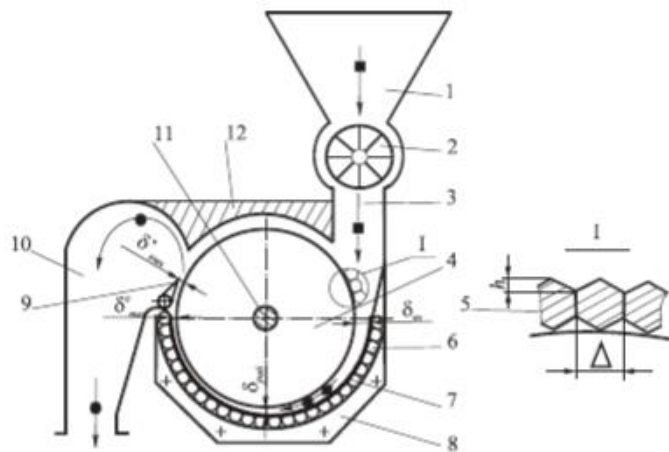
Скарифікатор [4]: 1-завантажувальний бункер, 2-валик, 3-завантажувальний отвір, 4-барабан, 5-вигляд внутрішньої поверхні барабану, 6-прокат круглий, 7-скарифікуюча поверхня, 8-дека, 9-надставка, 10-вихідний патрубок, 11-вал, 12-корпус
